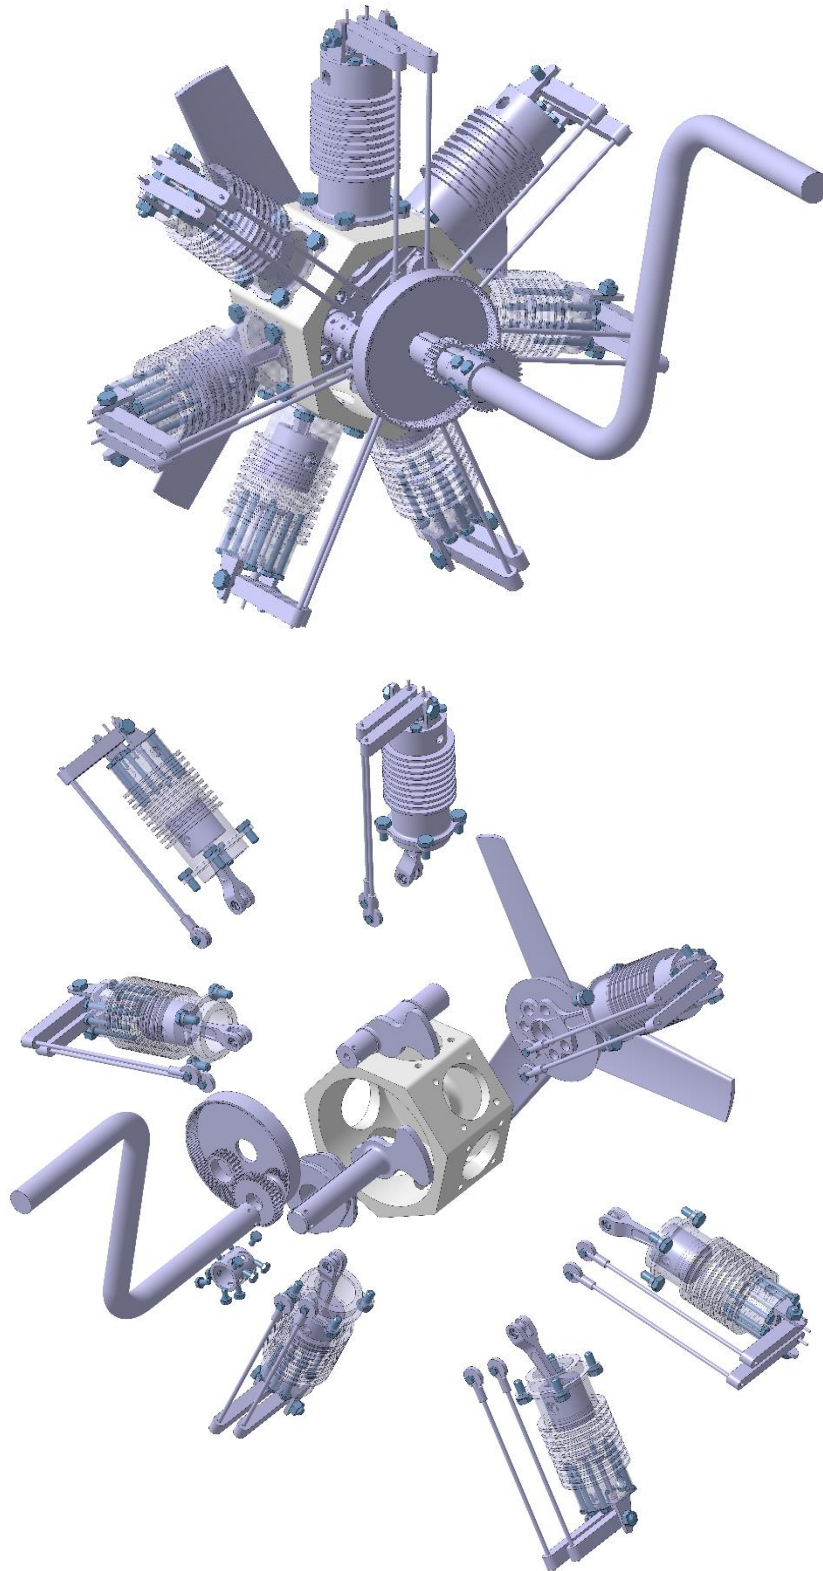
arriba: vista del conjunto al completo con la incorporación de la manivela de movimiento y el casquillo de unión. Abajo: vista explosionada del conjunto dividido por subconjuntos y los nuevos componentes añadidos.
